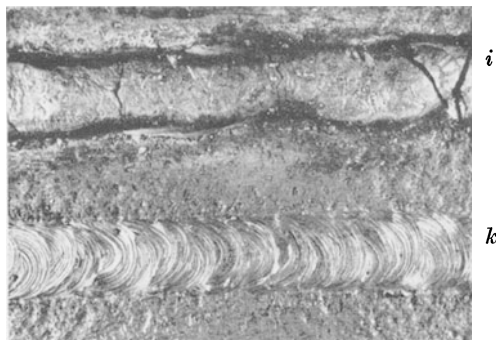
Aussehen von Schweißraupen mit und ohne Schlacke.
